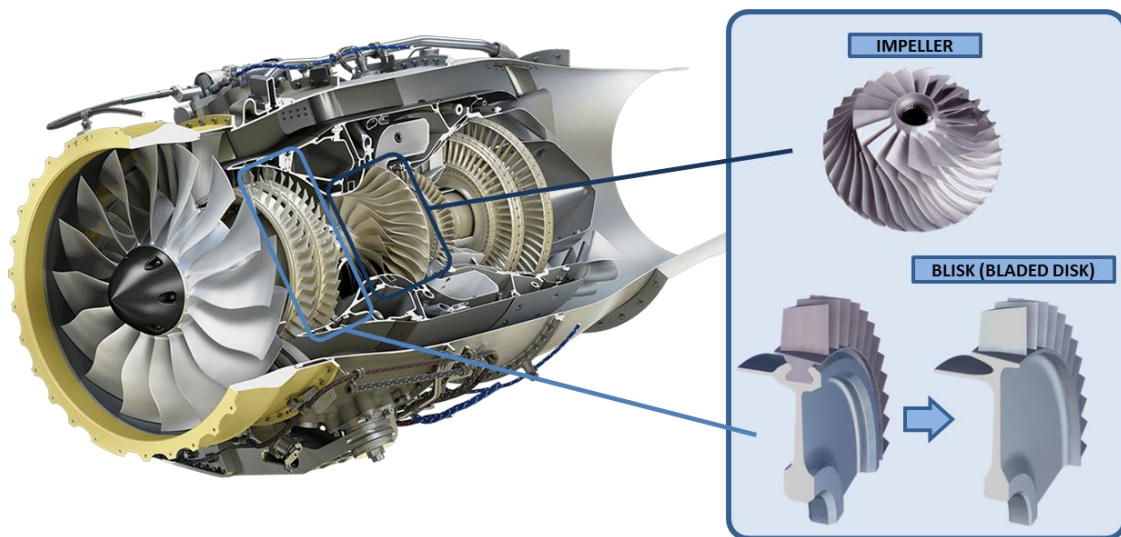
4 Imagen de blisks e impeller en el motor turbofan HF-120 (GE-Honda)
